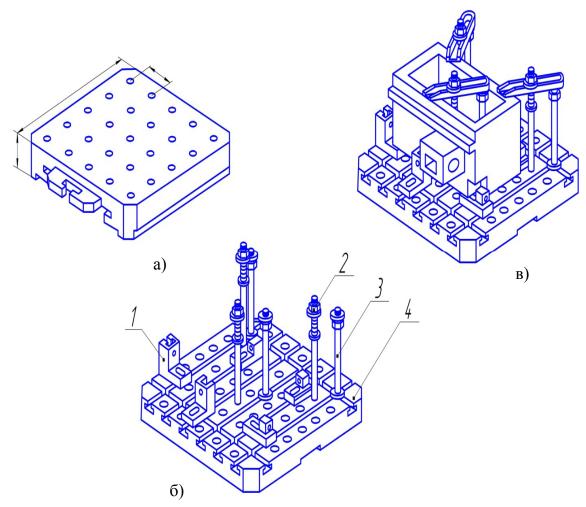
Приспособление-спутник; а — плита приспособления-спутника станка ИР 500МФ4; б — плита с закрепленным на ней приспособлением; в — приспособление в собранном виде с установленной заготовкой
